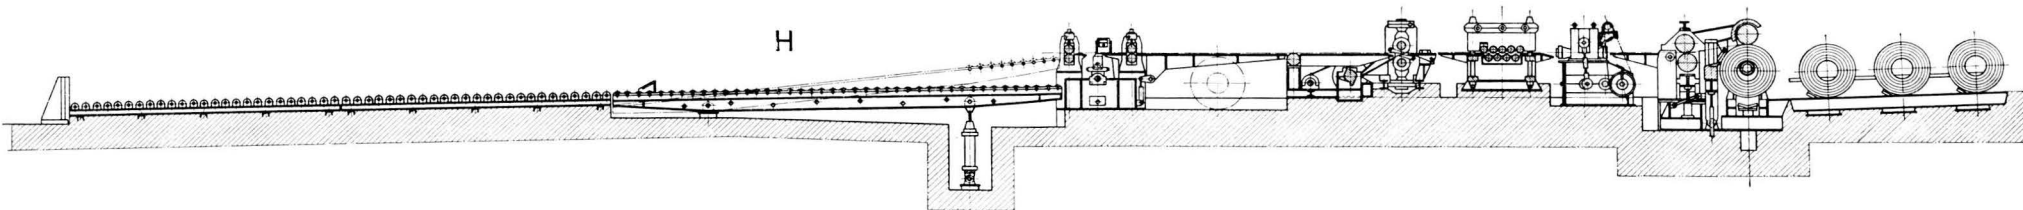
Linha de corte a frio para chapas médias bobinadas, fornecida a uma usina siderúrgica brasileira. Nesta instalação são cortadas chapas com espessura até 8 mm.
